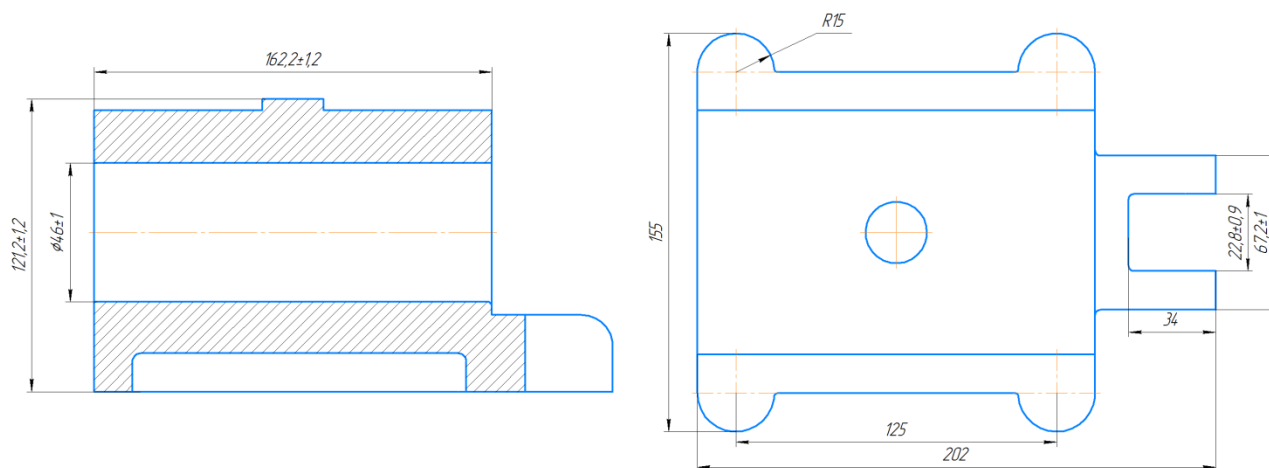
Ескіз заготовки виливок у піщані форми з ручною формовкою 9-го класу точності розмірів та мас, 3 –го ряду припусків
